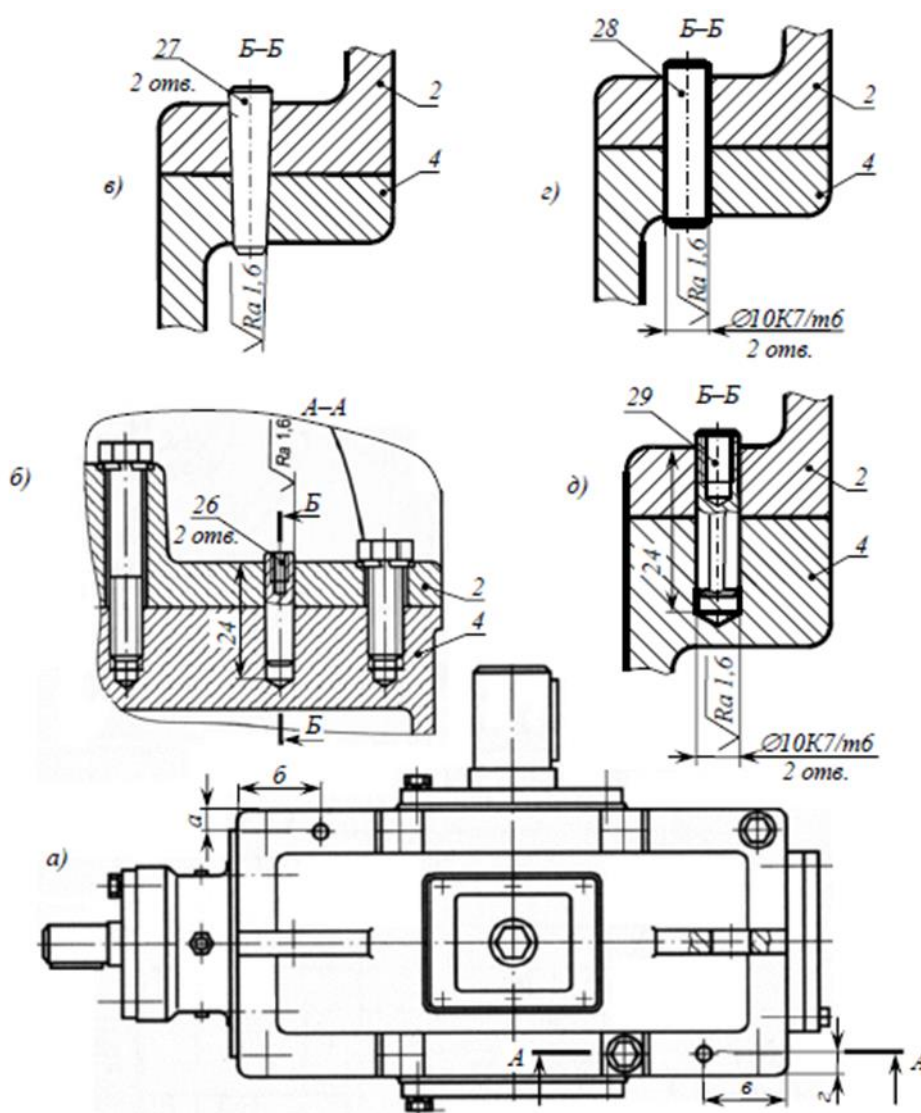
Пример изображения на сборочном чертеже отверстий под цилиндрические и конические штифты:
